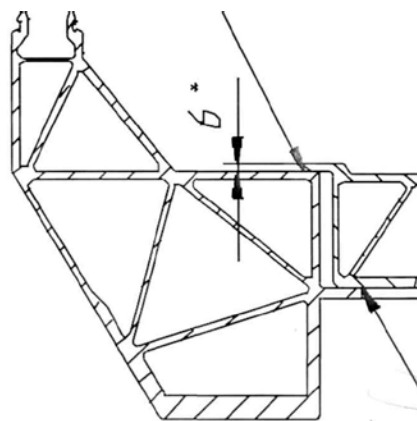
Эскиз сварного соединения настила
